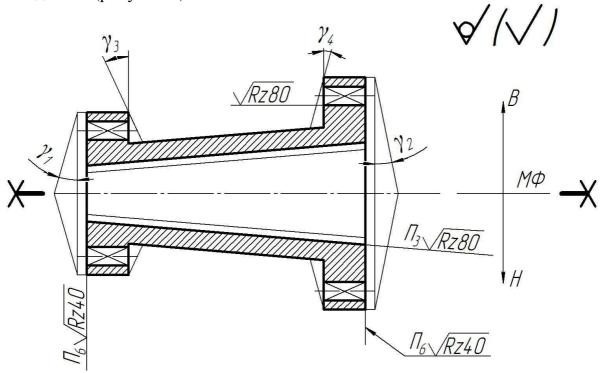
Эскиз детали с обозначением припусков и уклонов
